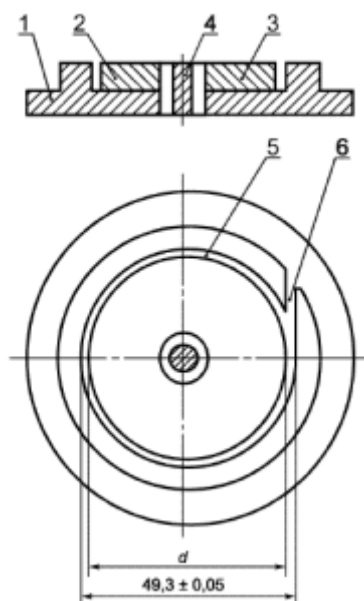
Держатель для образцов: 1 – корпус; 2 – цилиндрическая выточка; 3 – диск; 4 – штифт; 5 – кольцевая канавка; 6 – вспомогательная канавка
